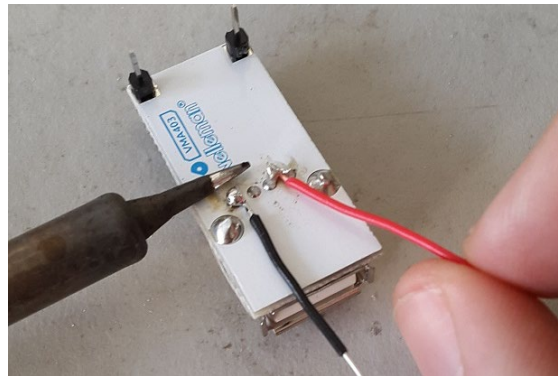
Soldadura de los cables del módulo de tensión de 5 V.
